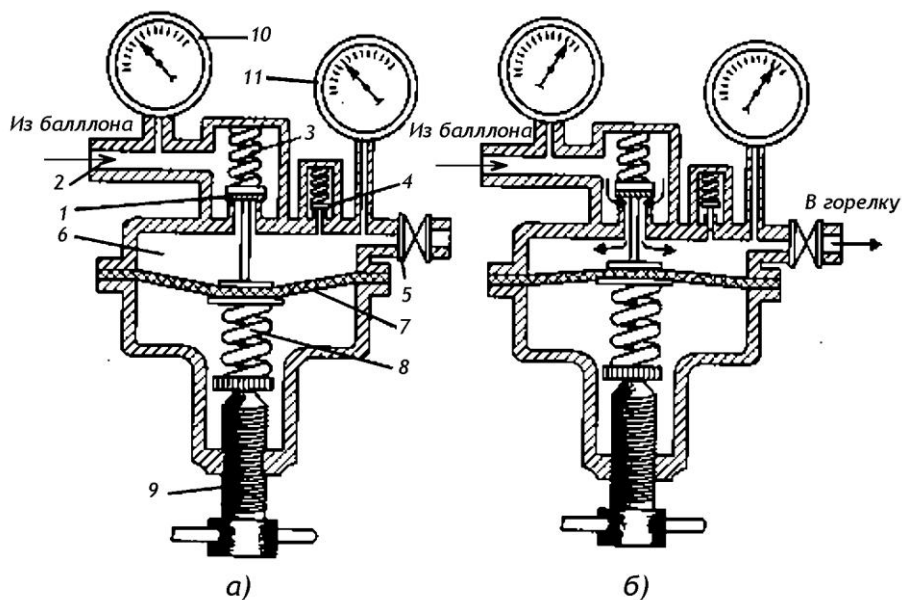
Схема устройства и работы редуктора, где а – газ не идет через редуктор; б – газ проходит через редуктор
